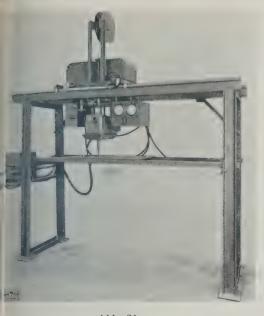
Selbsttätige Längsnaht-Schweißmaschine, Bauart SSW.
